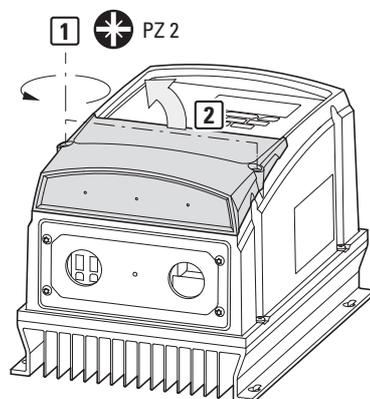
Gehäuseabdeckung entfernen (IP66)
